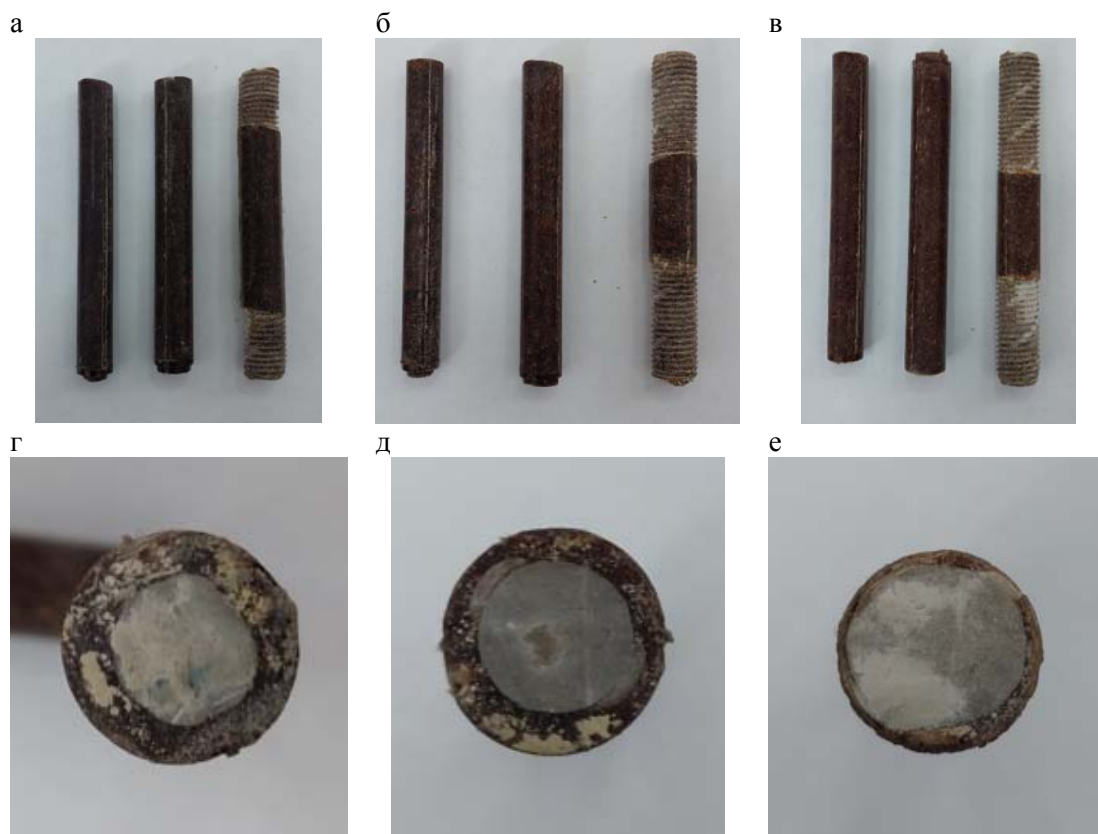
Общий вид стеклопластиковых заготовок для болтов:
